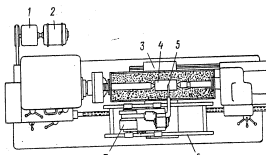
Схема установки сварочного аппарата АДС-1000 на станке.
